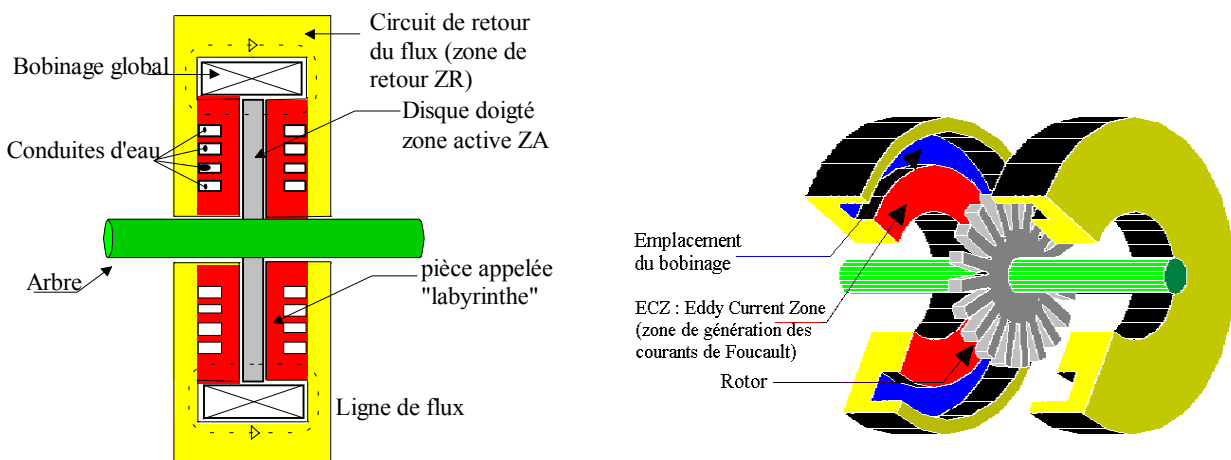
Coupe et vue 3D éclatée d'un frein
